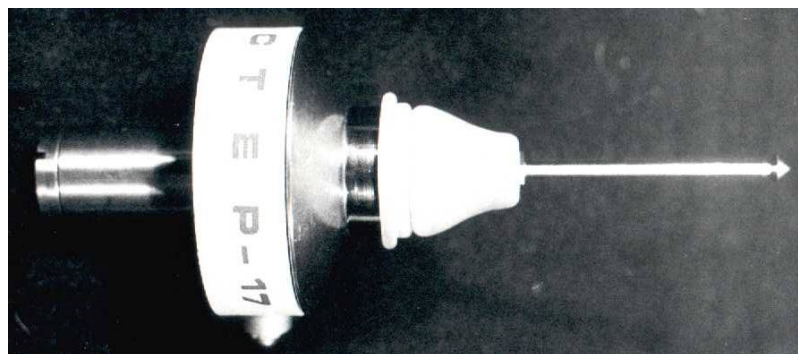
Вимірювальна головка «Майстер-17» як периферійний модуль загальної системи визначення координати торкання інструмента до поверхні деталі
